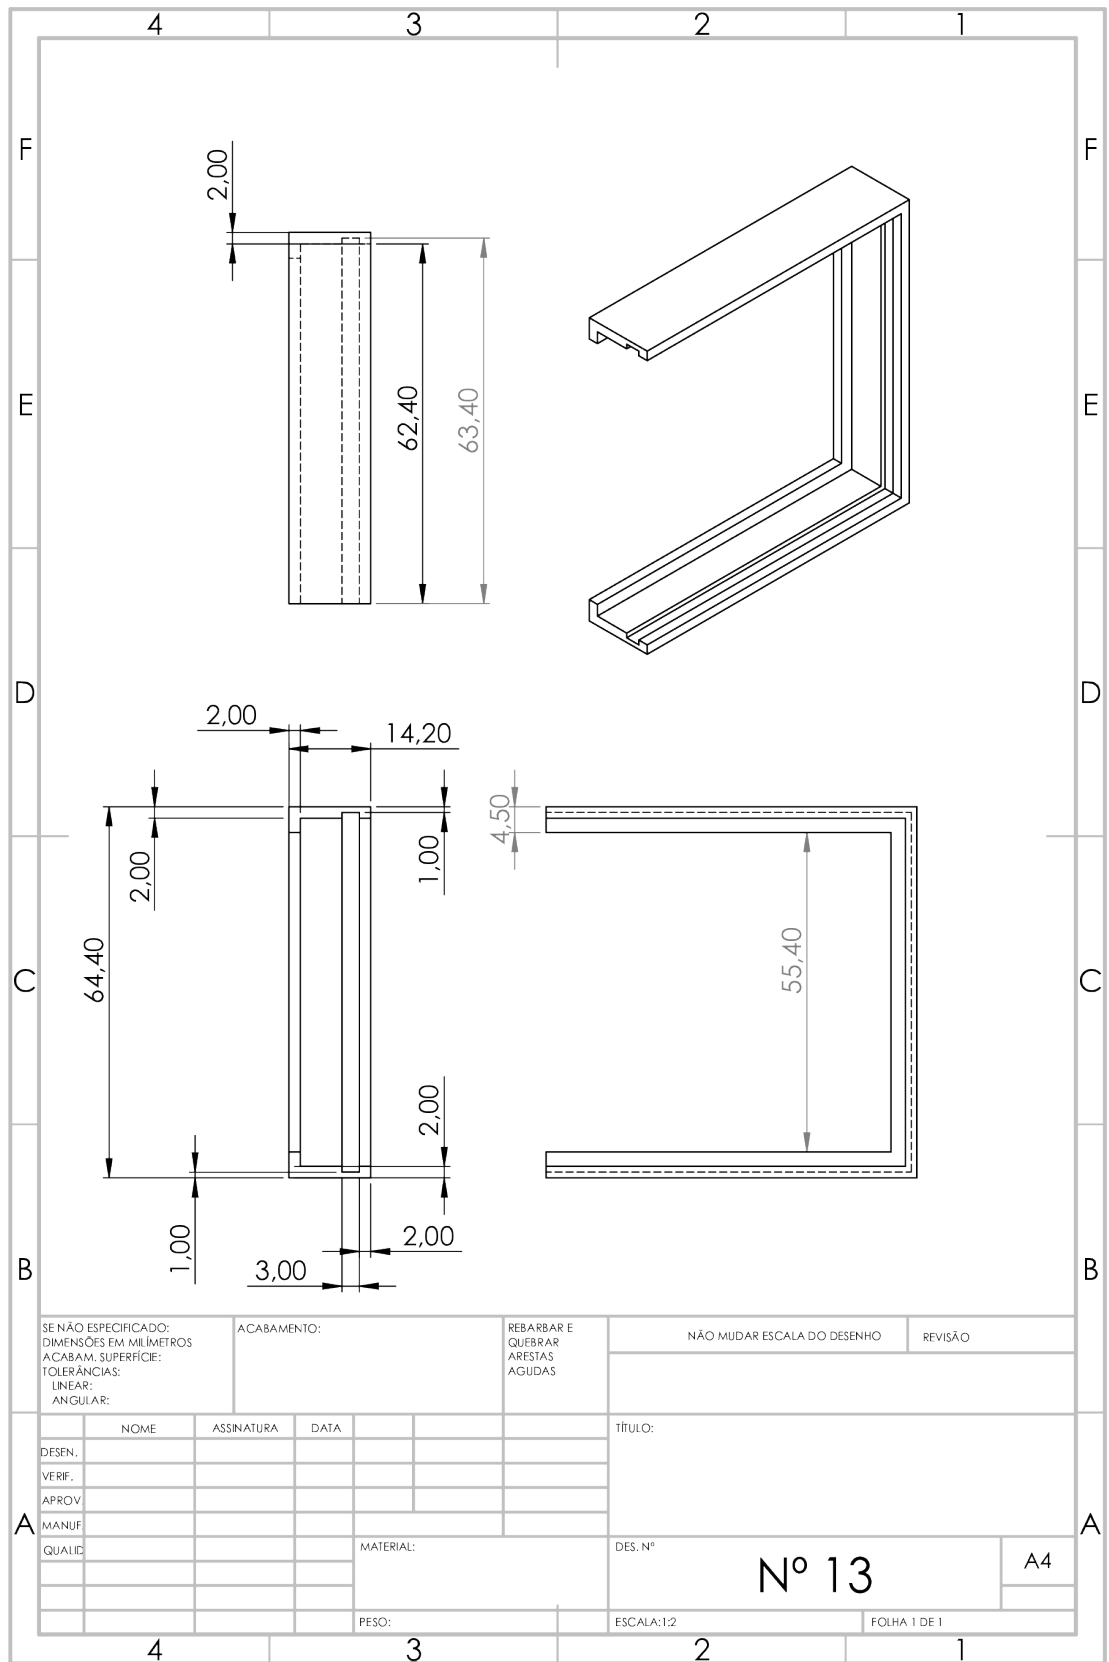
Desenho Técnico do Suporte de Difusor para Placa de LEDs do Microscópio
